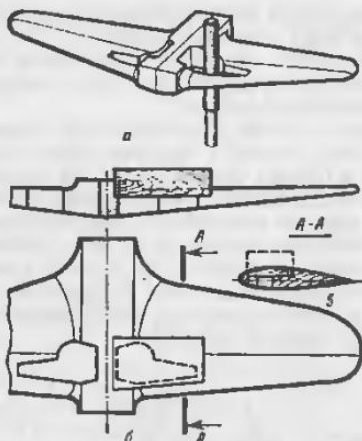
Один из способов изготовления колодцев убирающегося шасси: а - прорезка колодца насквозь; б - заклейка "пробкой"; в - обработка внешнего контура
